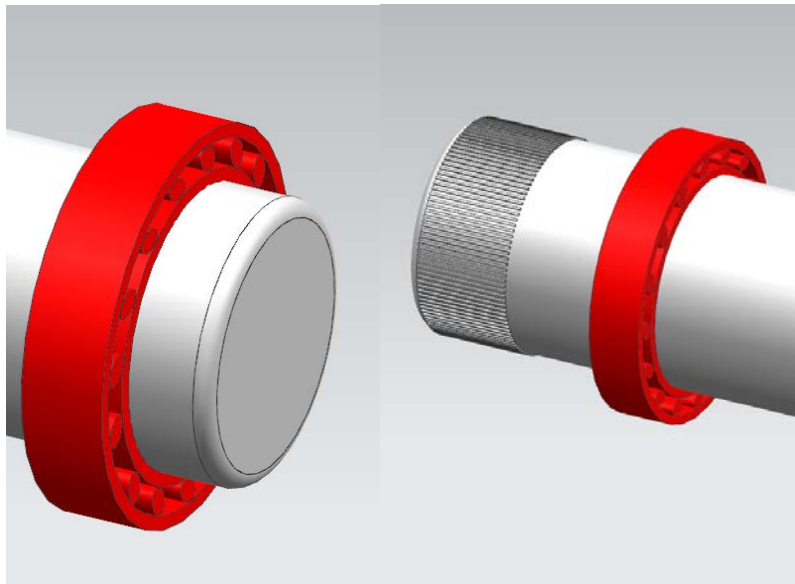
Rodamientos de rodillos cónicos NX 9.0
